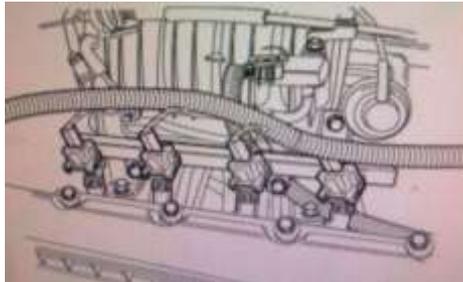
Desmontaje de los Sockets de los Inyectores
